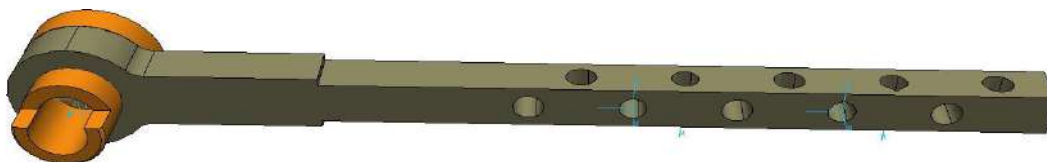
Калібрувальний інструмент для зварювального пістолета
